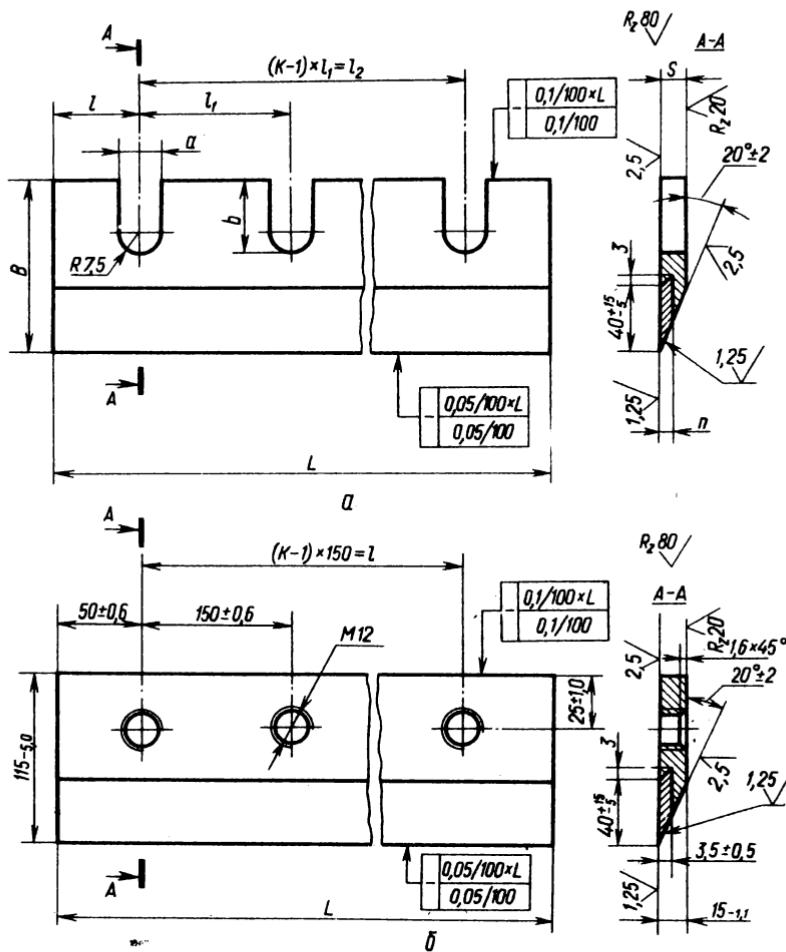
Конструкция ножей для резки шпона на ножницах:
